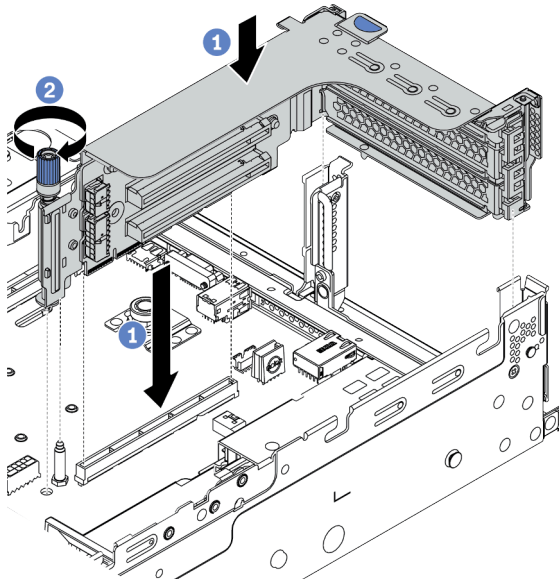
Installazione dell'assieme verticale 1/2 (staffa verticale a tre slot)
